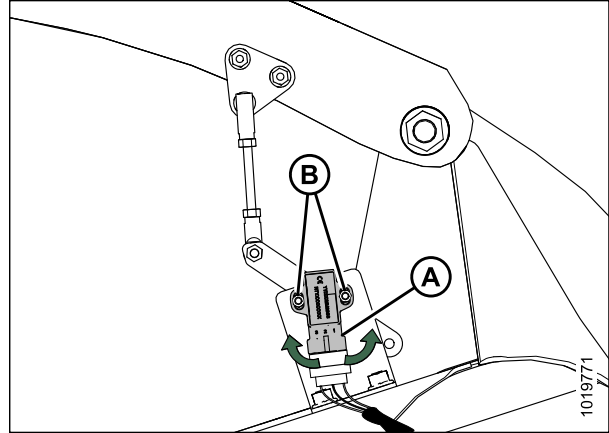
Sensor de altura do molinete – Braço direito do molinete (molinete elevado)
